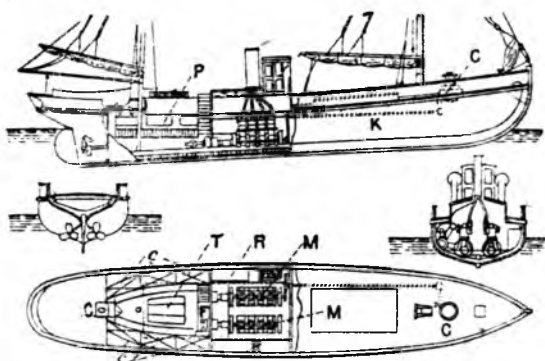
Планъ палубы и вертикальные разрѣзы промысловаго рыболовнаго судна съ двумя вспомогательными двигателями по 60 л. с.—С, кабестанъ отъ двигателя.—М, двигатель.—Р, каюта для экипажа съ диванами с.—К, кухня.—Т, трюмъ.—Л, резервуары для жидкаго топлива.
